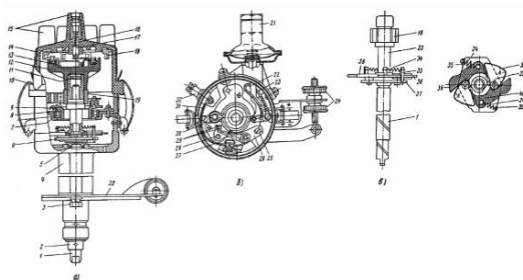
РаспределительР137: а–общий вид; б–центробежный регулятор; в–вид сверху; 1–вал; 2–муфта; 3–болт крепления октан -корректора; 4–корпус; 5–бронзовая втулка; 6–центробежный регулятор; 7–подшипник; 8–неподвижный диск; 9–подвижный диск; 10–зашелка; 11,30–филицы; 12–ротор; 13–резистор; 14–крышка; 15–выводы; 16–пружина; 17–контактный диск; 18–электрод крышки; 19–кулачок; 20–октан-корректор; 21–вакуумный регулятор; 22–тяга; 23–проводник, соединяющий подвижный диск с корпусом; 24–гайка; 25–эксцентрик; 26–держатель неподвижного контакта; 27–рычажок; 28–винт; 29– контакты; 31–проводник; 32–вывод; 33–втулка кулачка; 34–пружина; 35–стойка поводковой пластины; 36,37–поводковые пластины кулачка и грузиков; 38–грузик; 39–ось грузика; 40–штифт на поводковой пластине кулачка
